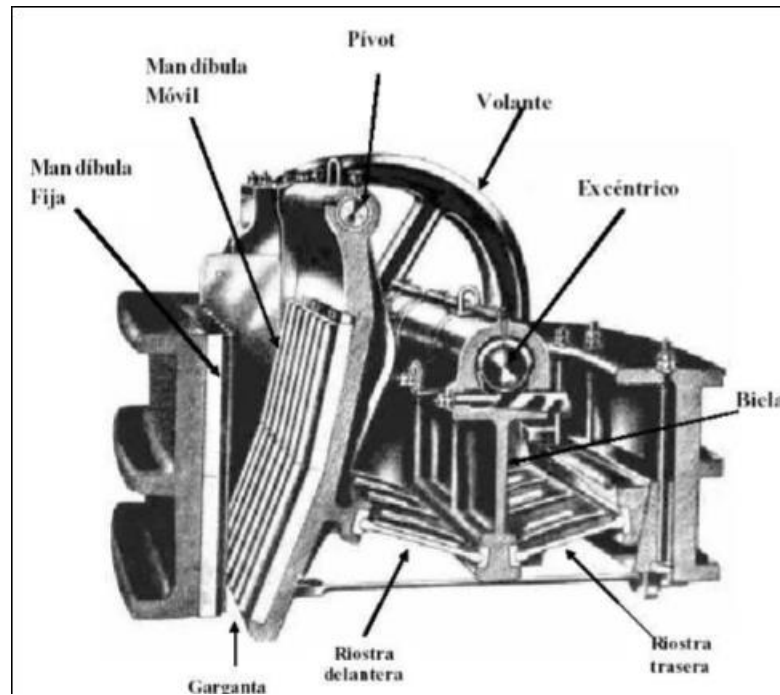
Partes de una machacadora de doble efecto o Blake.
